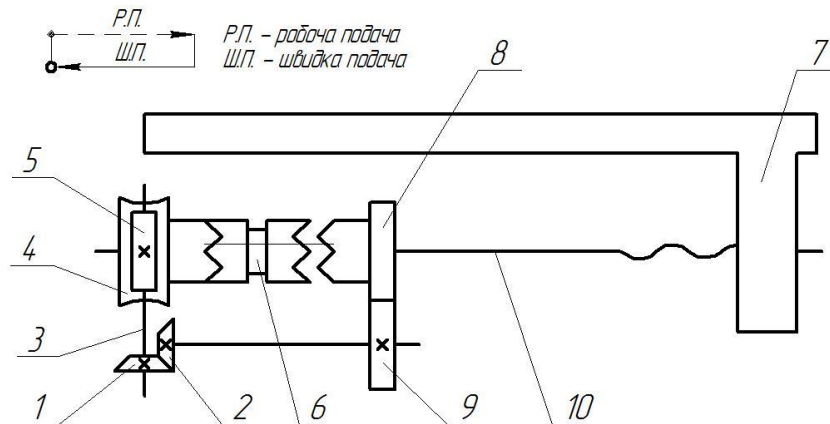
Кінематична схема механічного привода без реверсу: 1, 2 – конічна пара; 3 – ведучий вал; 4, 5 – черв’ячна передача; 6 – муфта; 7 – виконавчий орган; 8, 9 – циліндрична передача; 10 – ходовий гвинт
